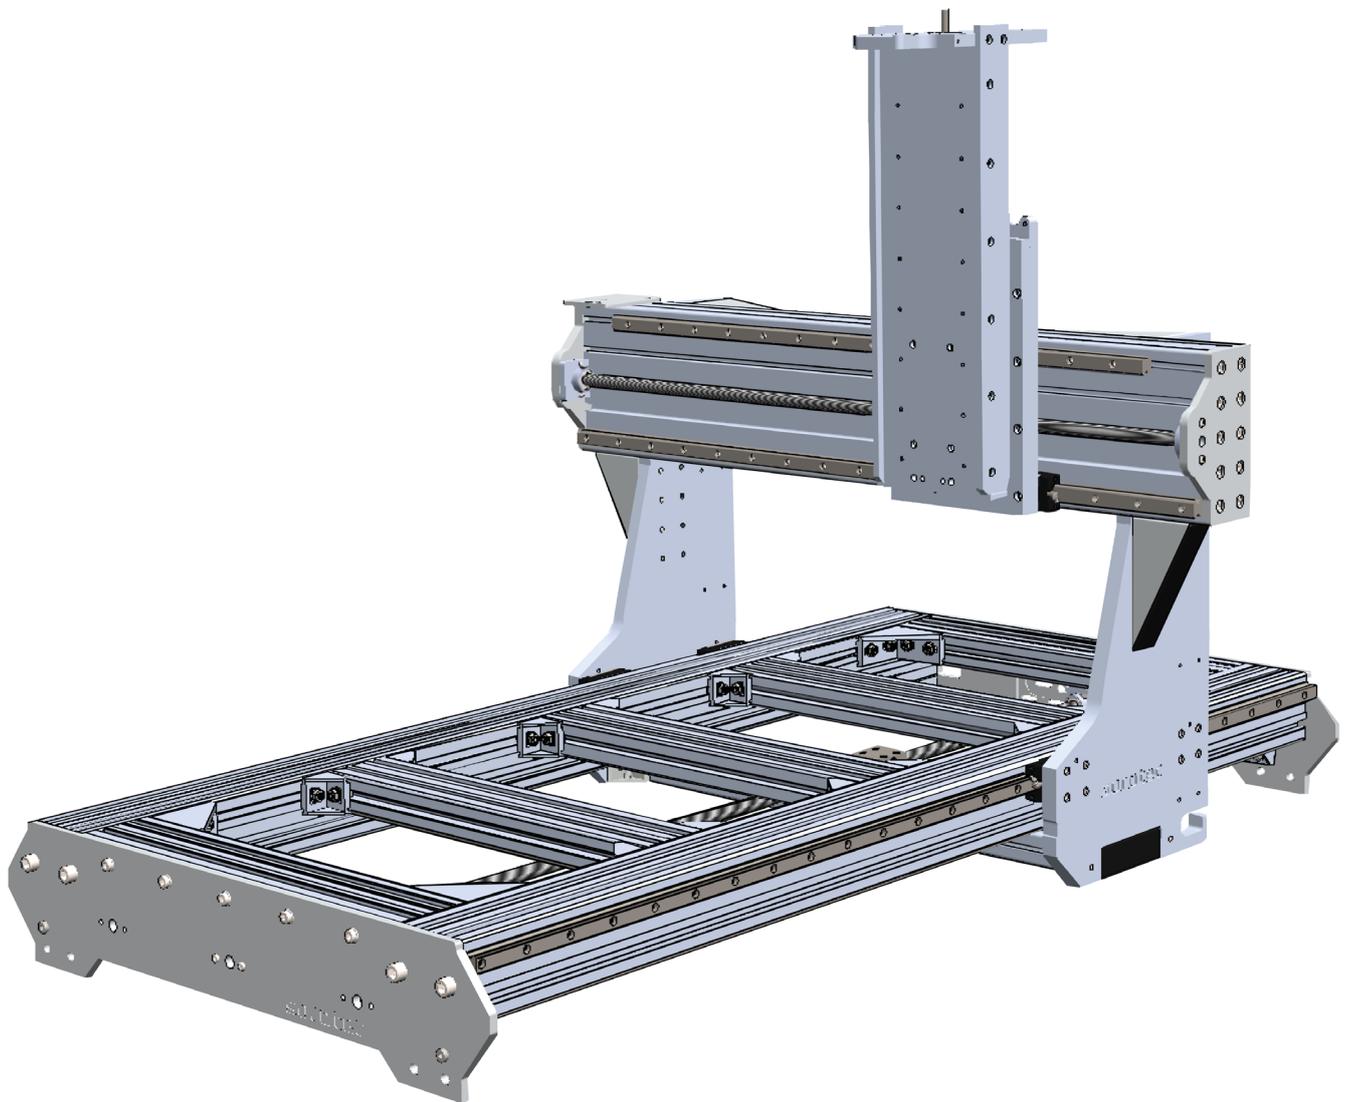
Mechanisch komplett aufgebaute Alu-Line
